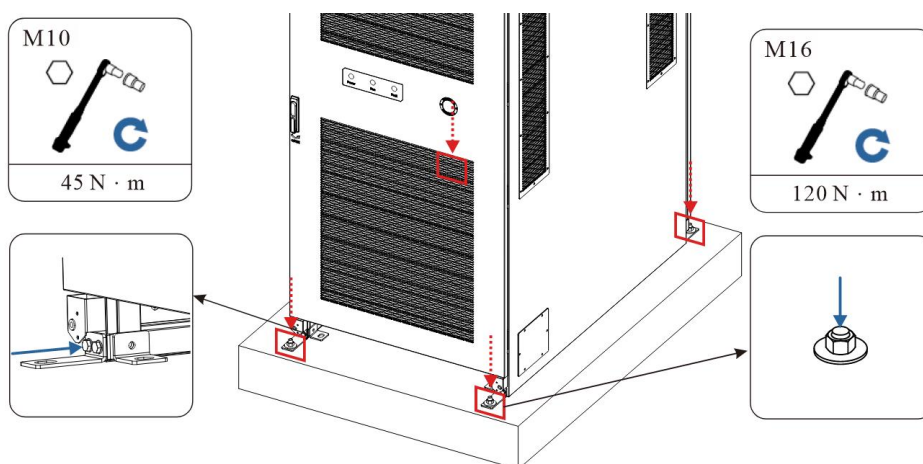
Installieren Sie die Befestigungen des Gehäuses (Blechteile) und montieren Sie die Plattform
